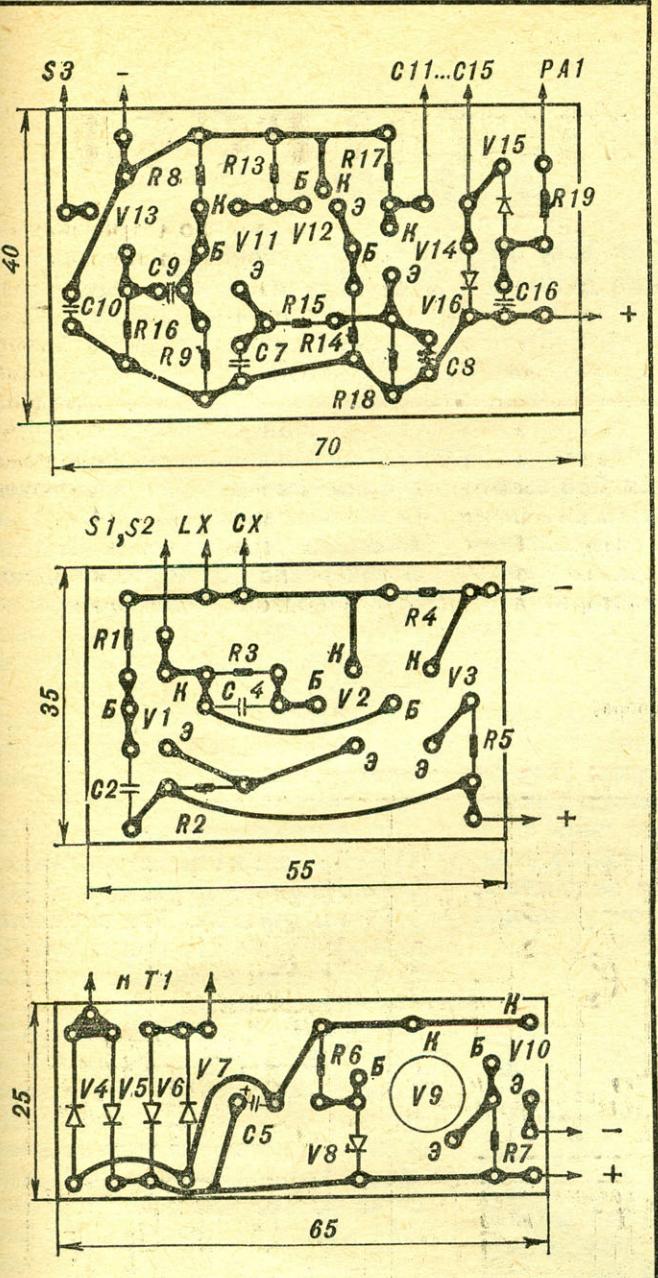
Печатные платы с расположением деталей: частотометра, генератора и блока питания.
